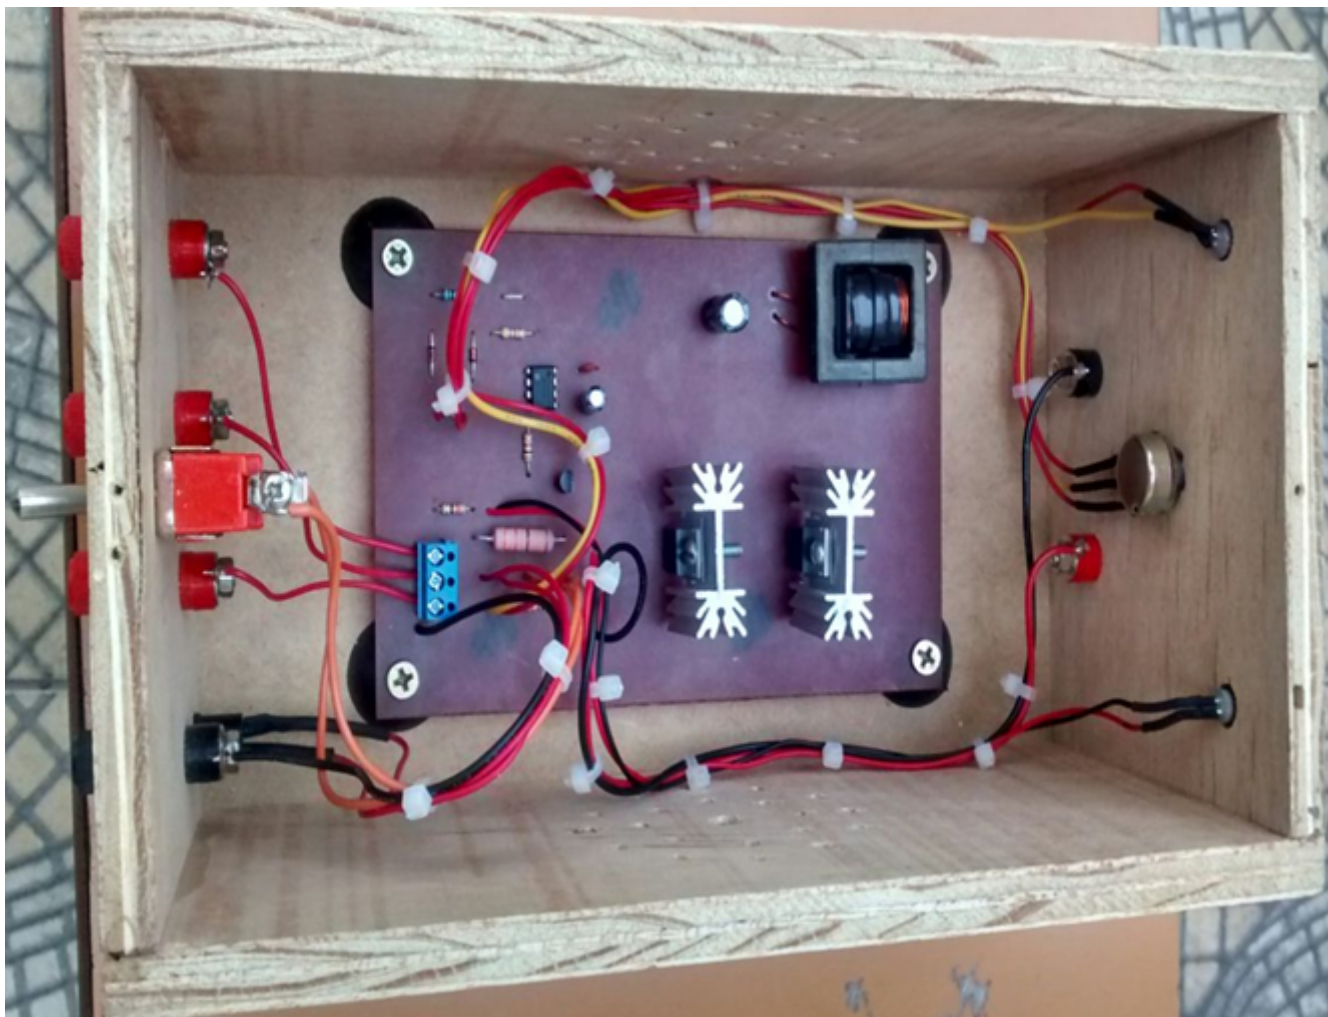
PWM, circuito driver e conversor Buck soldados na placa.
